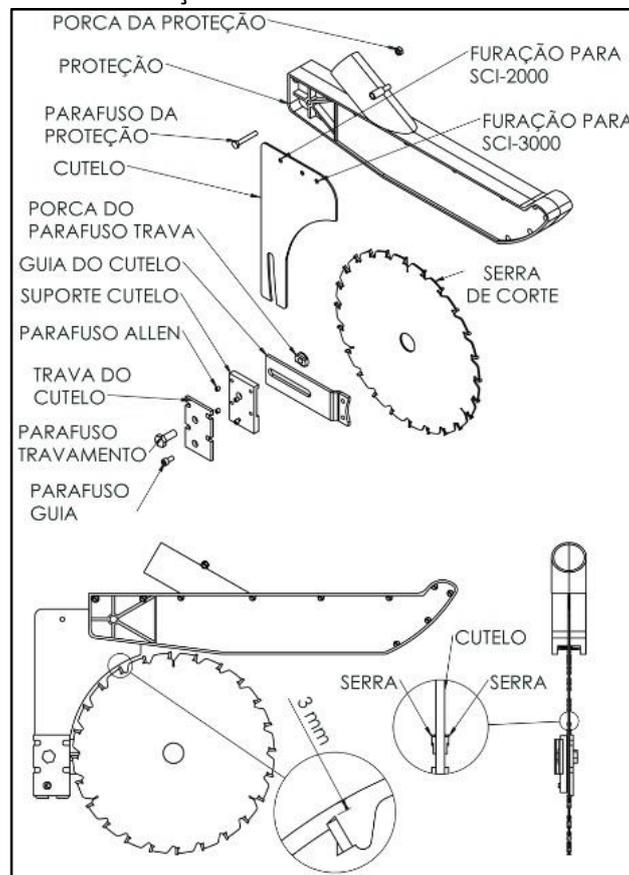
REGULAGEM CONJUNTO PROTEÇÃO DA SERRA
